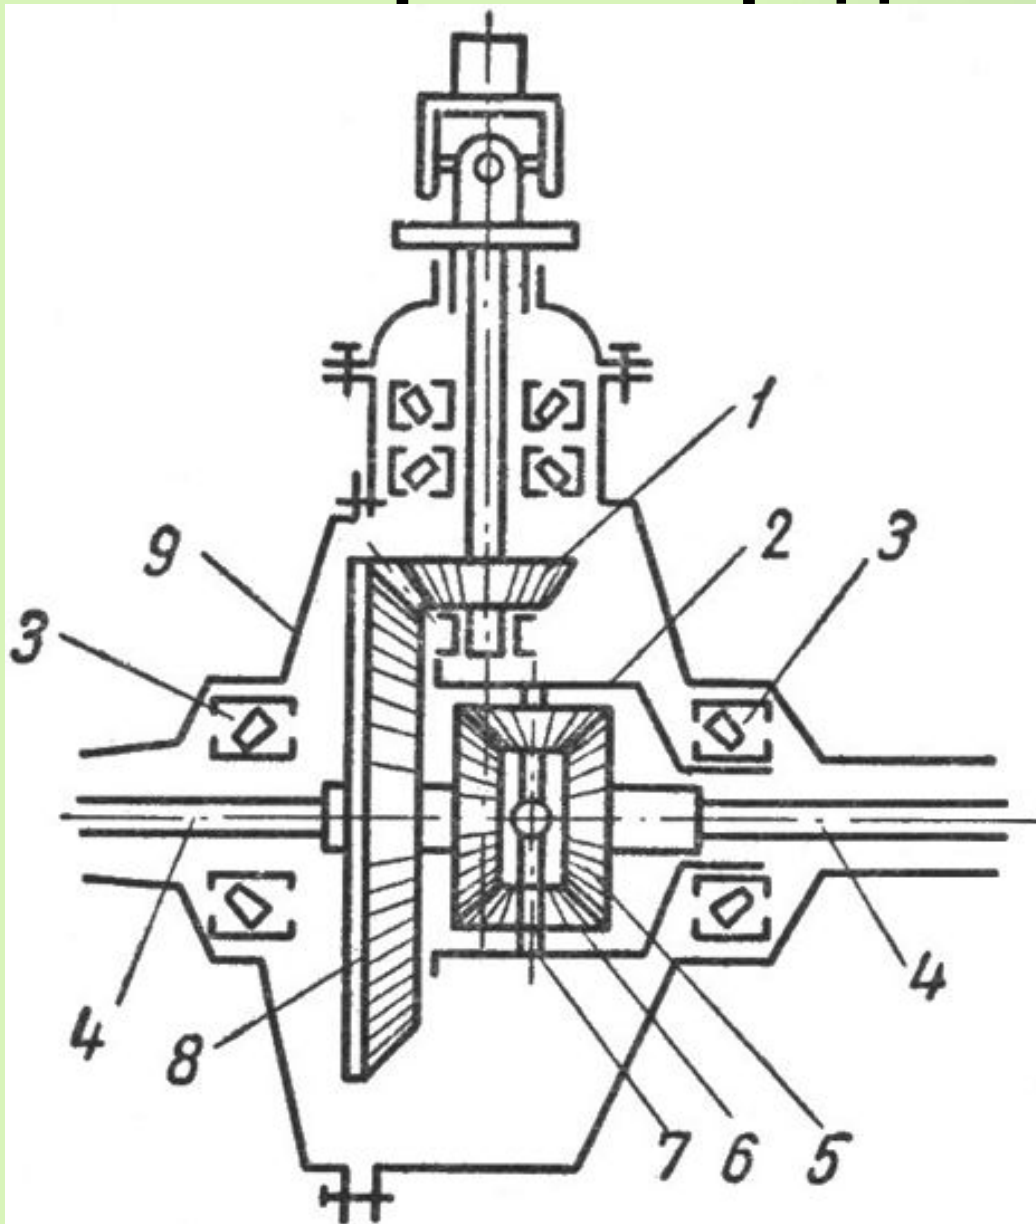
Схема дифференциала: 1,5,8 – шестерня; 3 – подшипник; 4 – полуось; 6 – сателлит
